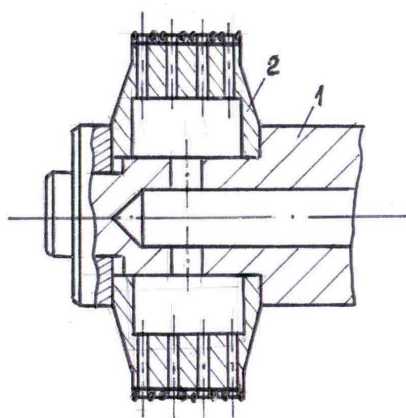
Схема устройства для подачи СОЖ через отверстия ролика в зону резания: 1 – оправка, 2 – ролик алмазный
